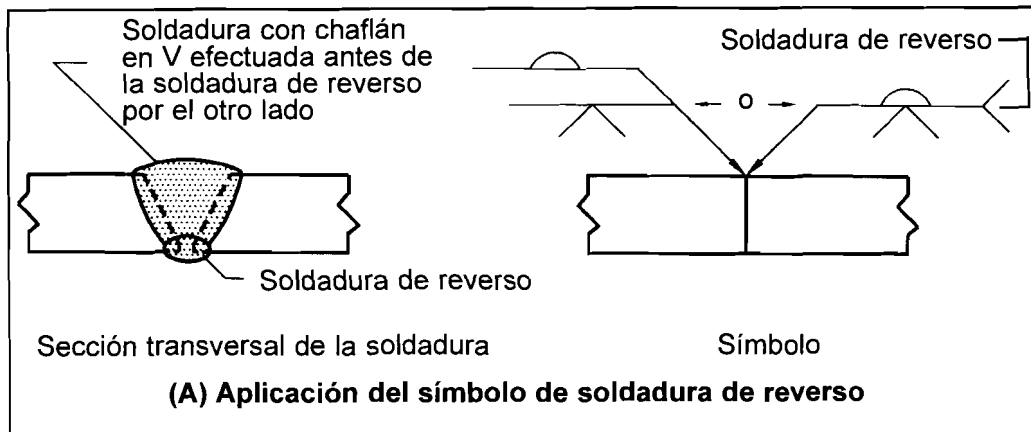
APLICACIONES DEL SÍMBOLO DE SOLDADURA DE REVERSO O RESPALDO
